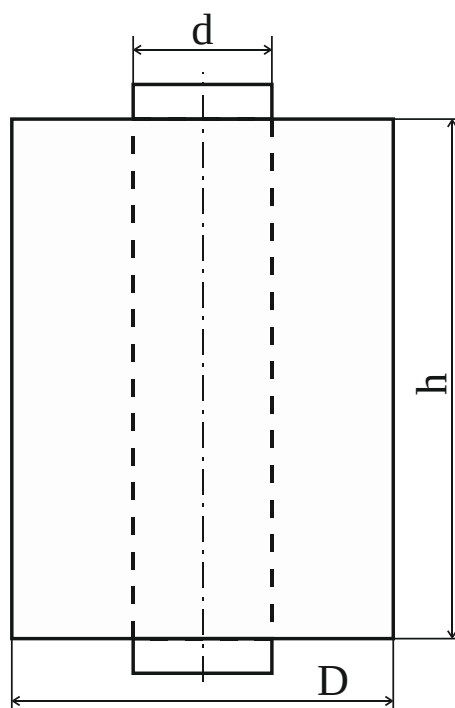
Цилиндрическая бобина крестовой намотки
